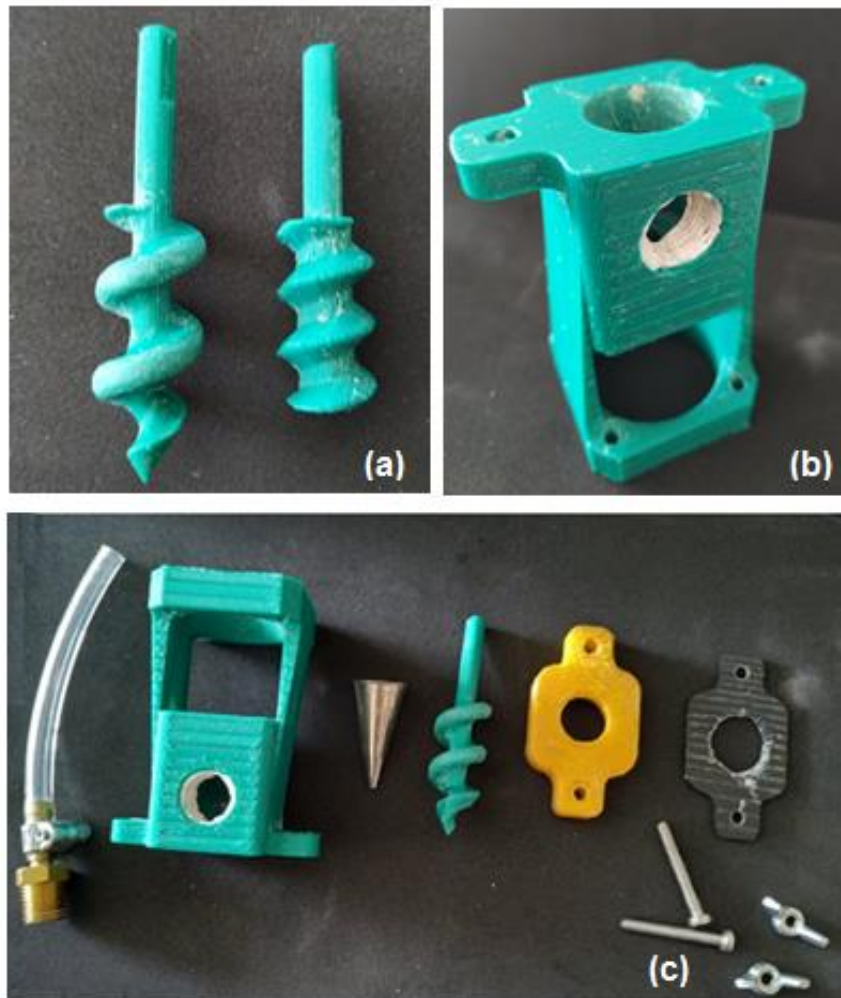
Prototipo primario de extrusor, (a) tornillos sin fin, (b) base del extrusor, (c) partes del extrusor de izquierda a derecha: Boquilla de entrada de arcilla, base del extrusor, boquilla de salida del material, tornillo sin fin, pieza del cierre del extrusor, empaque y pernos
